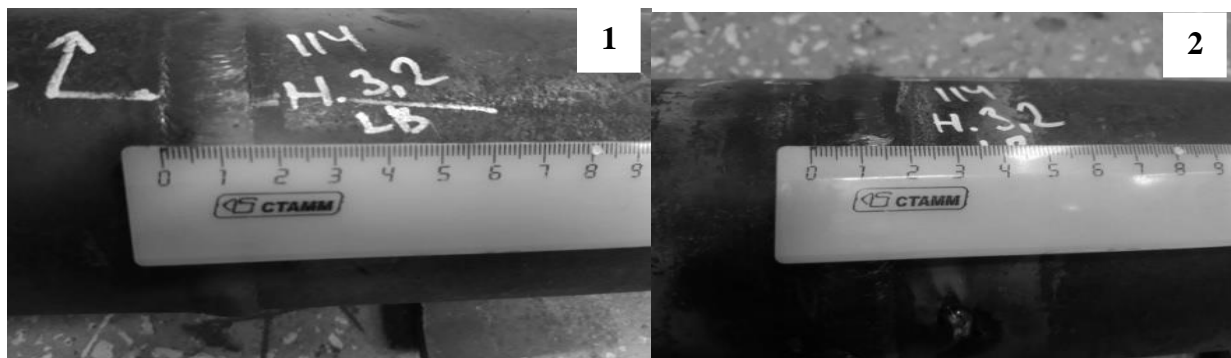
Сварное соединение 1. Рисунок Б22. Сварное соединение 2.
